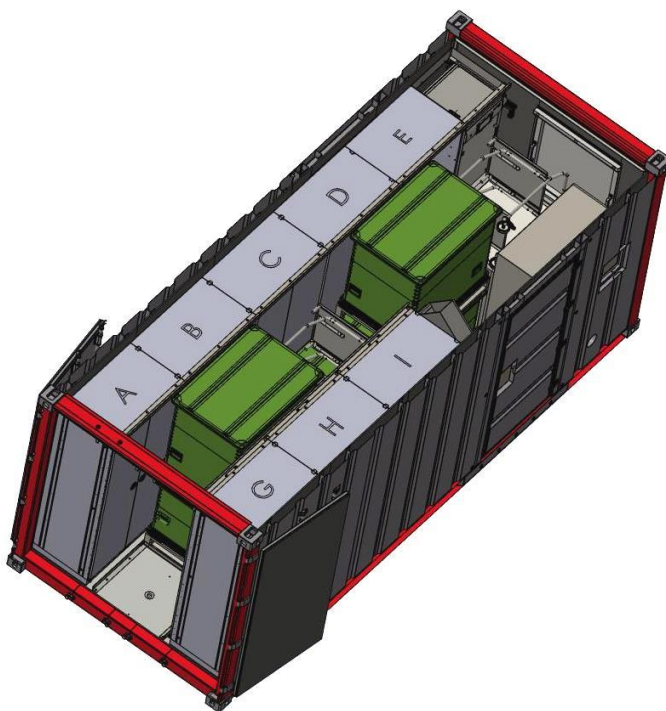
Platzierung von Sterilisator 65 TC und Spülschrank mit Einbau-URG
